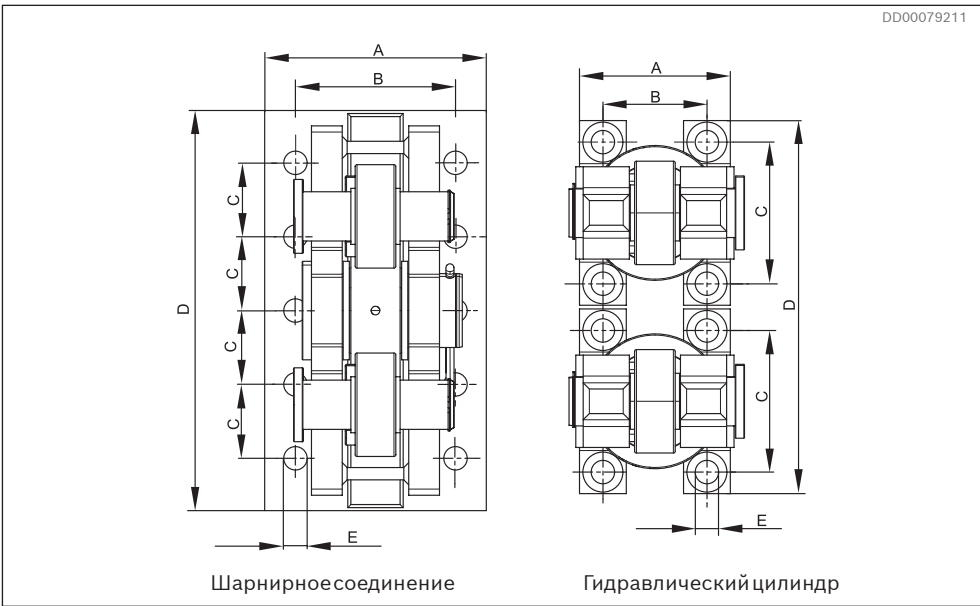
Расположение отверстий для шарнирного соединения и гидравлического цилиндра при использовании DTCBM 4600 – DTCBM 6000
